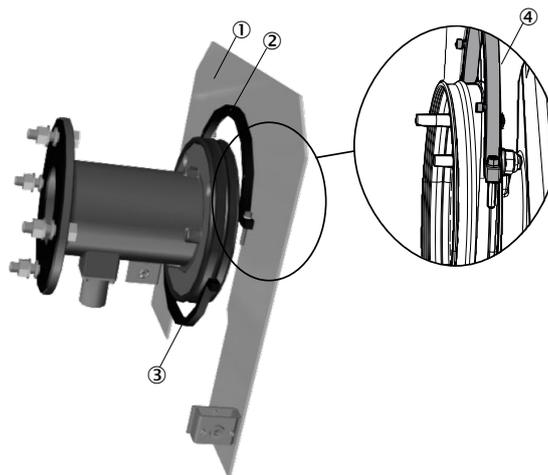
Detailansicht: Oberen Befestigungsring auf der Seite des Spülluftvorsatzes aufsetzen
